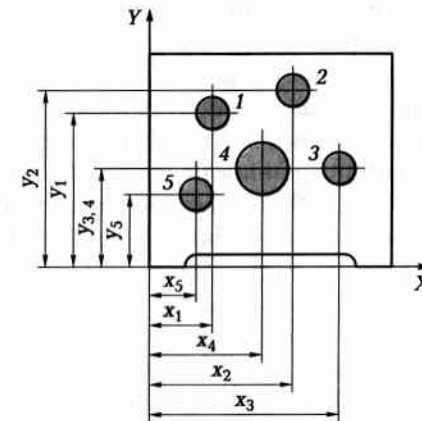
Схема обработки отверстий 1—5 в корпусной детали по координатам:
